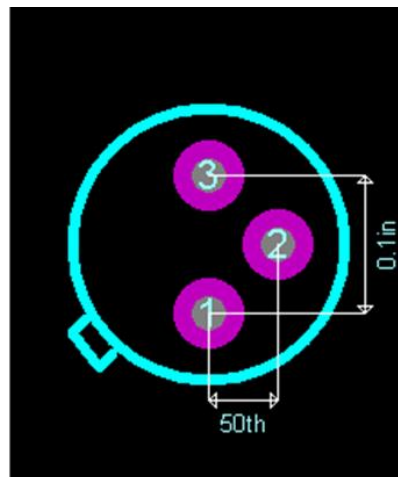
Vista previa de la implementación en placa PCB del encapsulado TO46-3 [26].
